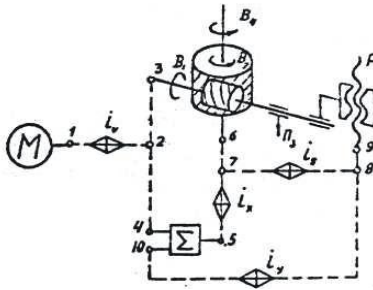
Структурна схема зубофрезерного верстата
